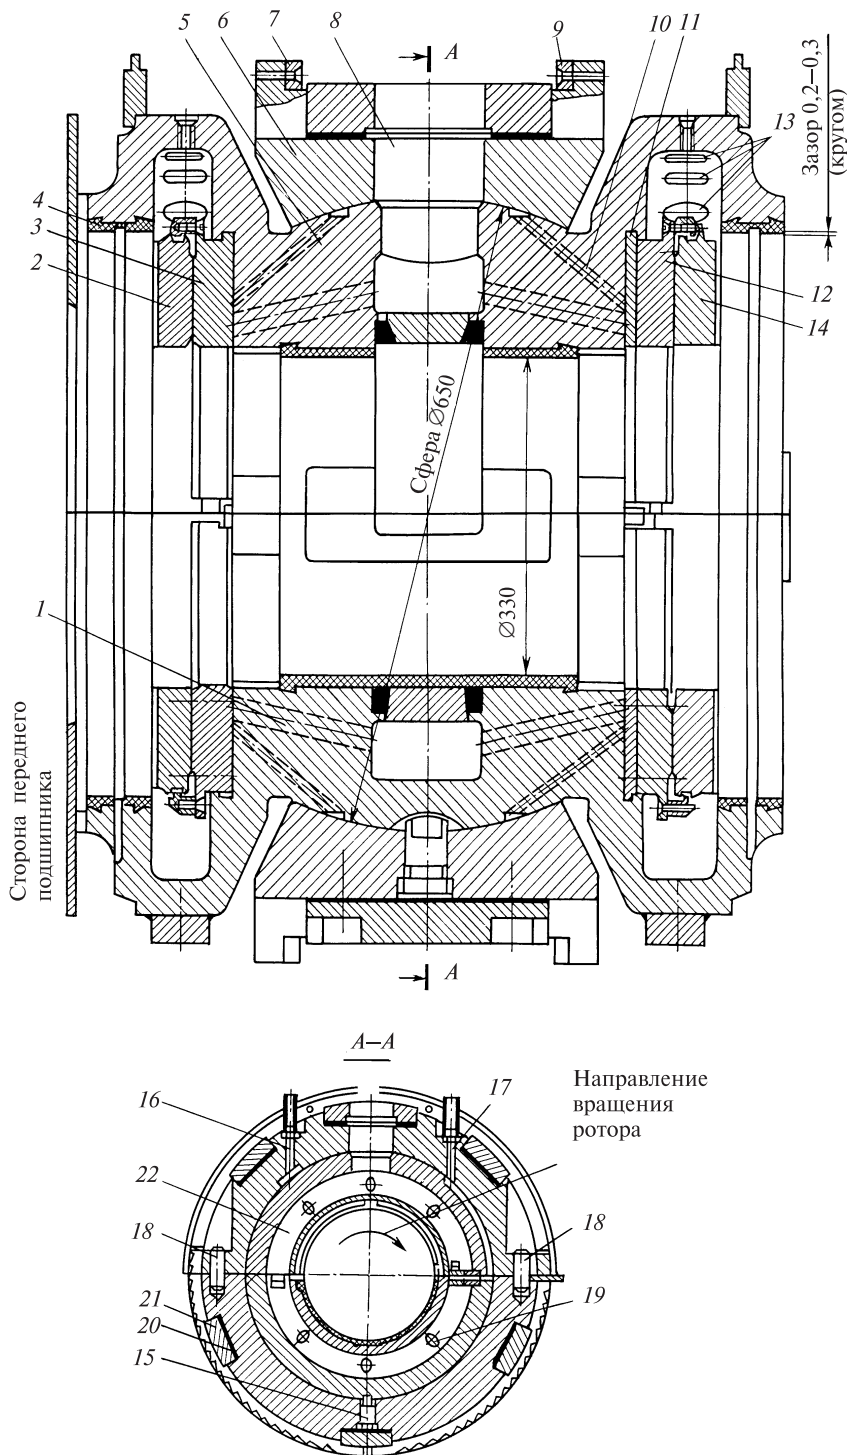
Опорно-упорный подшипник турбины Т-250/300-23,5 ТМЗ
